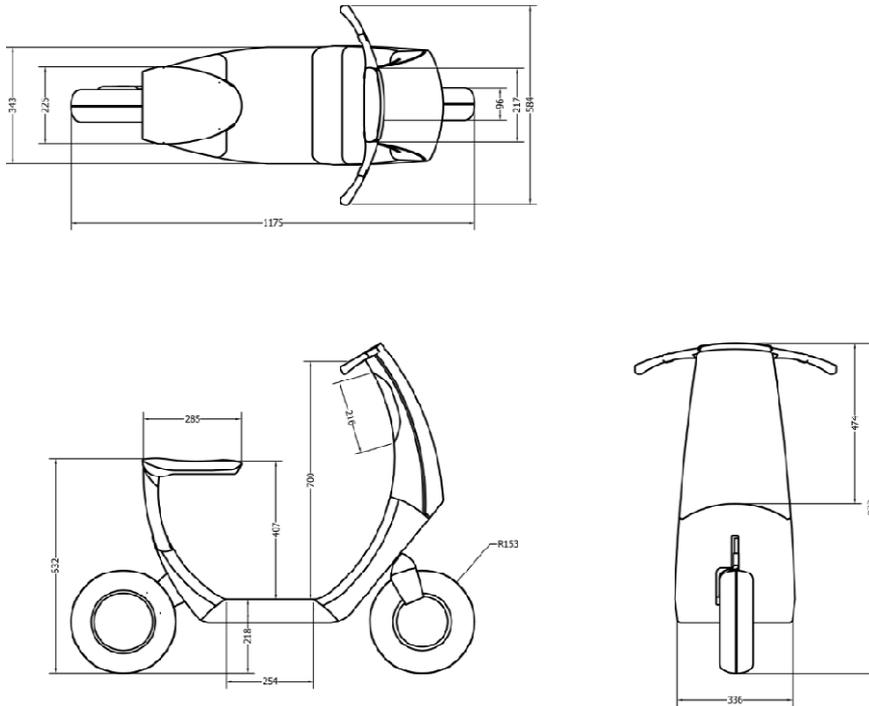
Fast Track con las dimensiones de la moto (desplegada).
